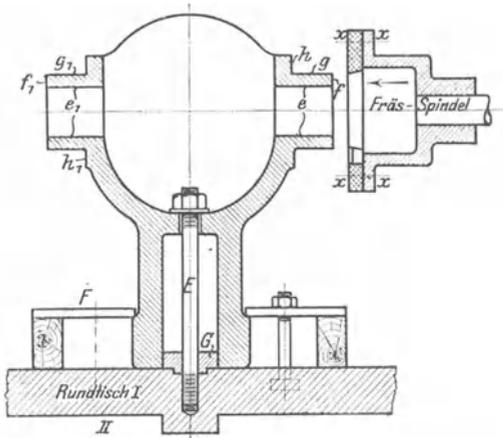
Bearbeitung der Zapfen für die Schuhe.
